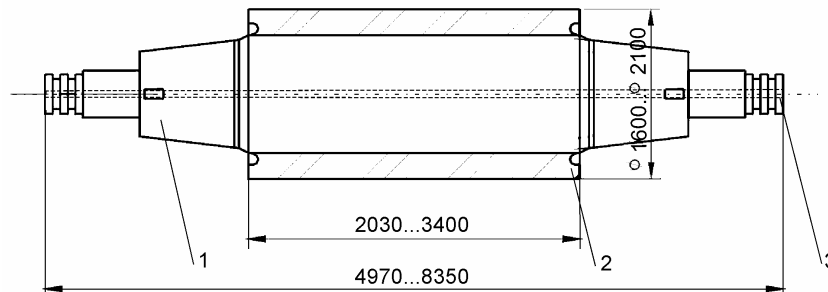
Базовая конструктивная схема составного крупногабаритного прокатного валка: 1 - ось валка; 2 – бандаж (втулка); 3 – пробка оси
